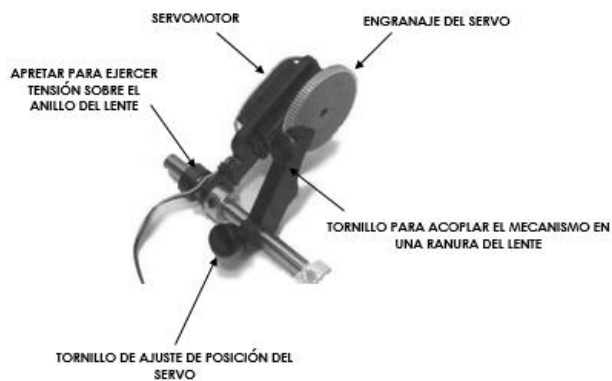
Pieza mecánica que permite acoplar el servo al anillo del lente. [73]
